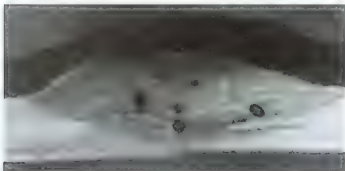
Поперечный разрез сварного шва, отмеченные скоплениями пористости. Этот сварной шов выполнен на 300-миллиметровом диаметре трубной заготовки, изготовленной из углерода. Вспомогательное электропитание: Eutaw Electric, Delavan, New York Pressure Vessels and Piping, под давлением 100 фунтов на квадратный дюйм (работы выполнялись на территории завода New York Tube and Piping Company, Inc.).
